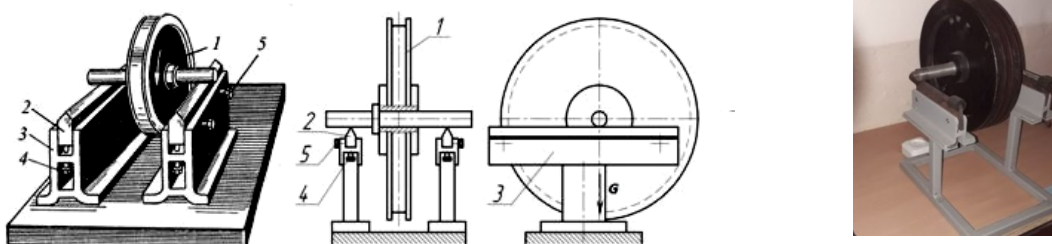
Схеми та світлина установки деталі на призмах: 1 – деталь; 2 – призми; 3 – стійки; 4 – гвинт регулювальний; 5 – гвинт стопорний
